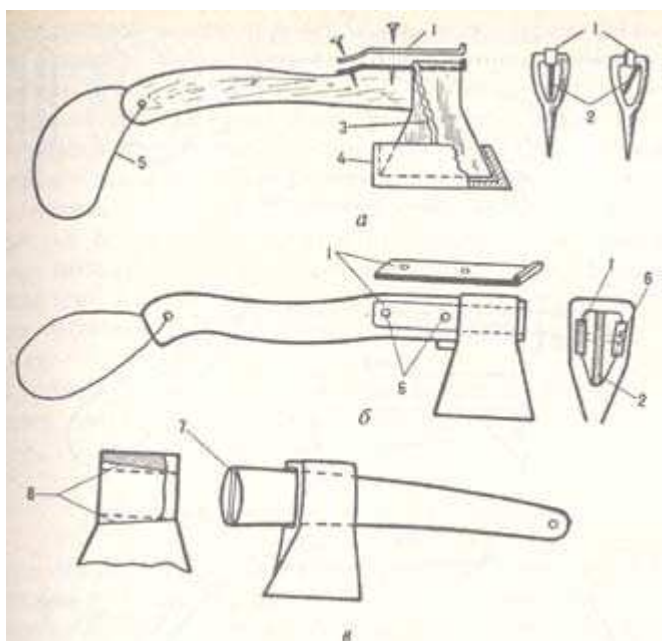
Варианты упрочненной насадки топоров на топорщицах: а — с помощью верхней пластины; б — с помощью двух боковых пластин; в — с предварительной расточкой на конус отверстия для топорщицы в топоре. 1 — пластины; 2 — клинья; 3 — резинка; 4 — чехол на лезвие топора; 5 — темляк; 6 — болтики; 7 — распил для клина; 8 — конусная расточка.
